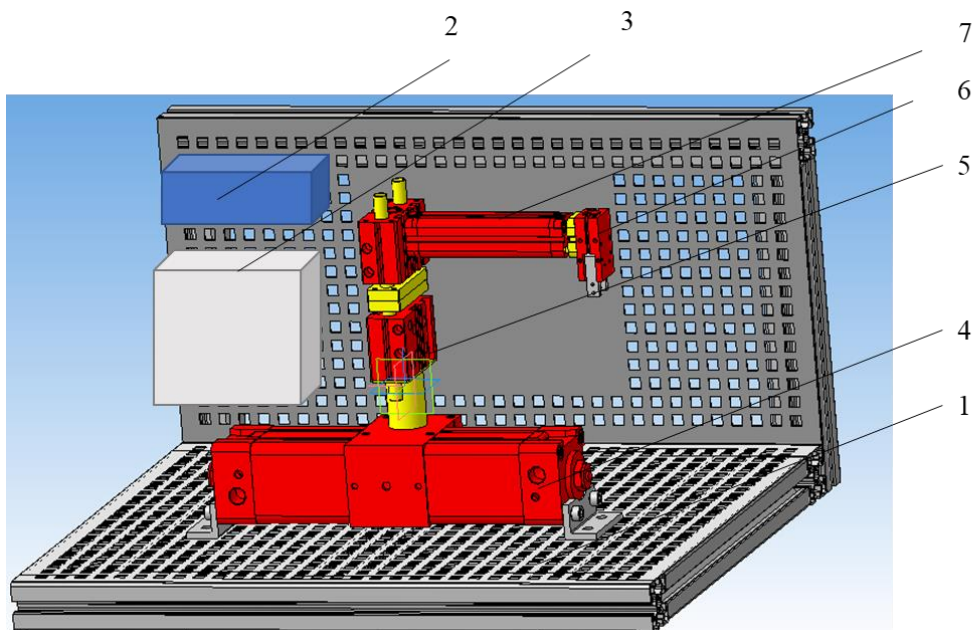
Загальний вигляд синтезованої конструкції РМ: 1 – станіна; 3 – шафа керування; 2 – ПЛК; 4 – циліндр поворотний пневматичний серії 69 (Camozzi); 5 – циліндр пневматичний QCTB із системою протиповоротною; 6 – захват пневматичний; 7 циліндр пневматичний серія 31(Camozzi).
